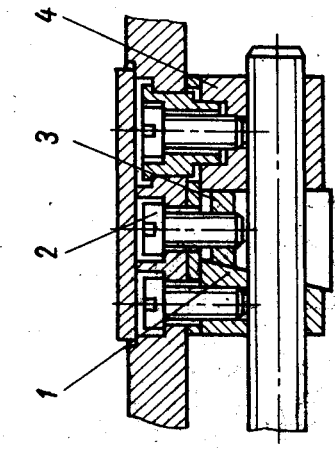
Регулировка зазора в резьбовом соединении винта и гайки 1 и 4 (рис.26) устраняется затяжкой клина 3 винтом 2.
